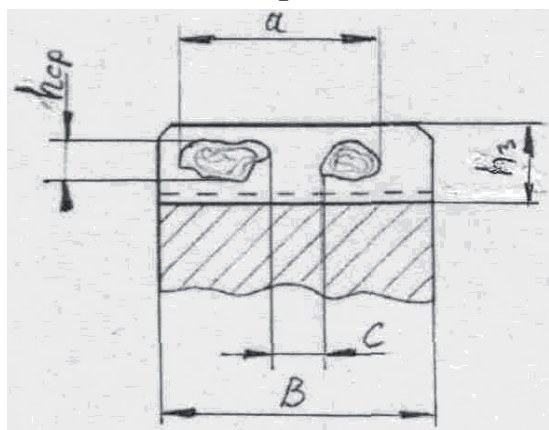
Суммарное пятно контакта на боковой поверхности зубчатого колеса
